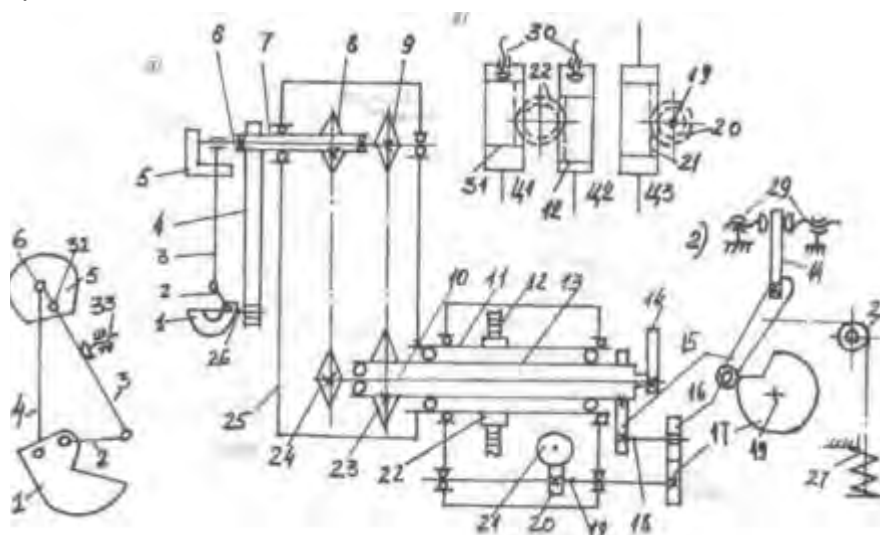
Кинематическая схема манипулятора для заливки металла
